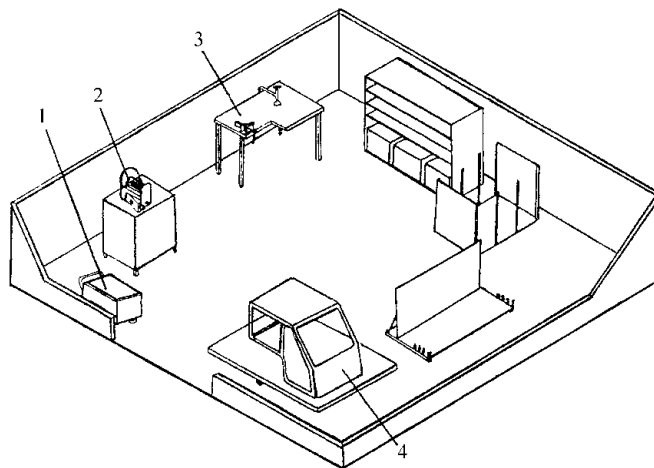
Жерстяницька дільниця: 1 – комплект інструментів і пристосування з гідроприводом для редагування І-332; 2 - настільна установка для різання тонколистового металу ОР-12624; 3 – верстак слюсарний з настільно-свердлильним верстатом Р-175; 4 – верстак слюсарний для жерстяницьких робіт ОРГ-5105.
